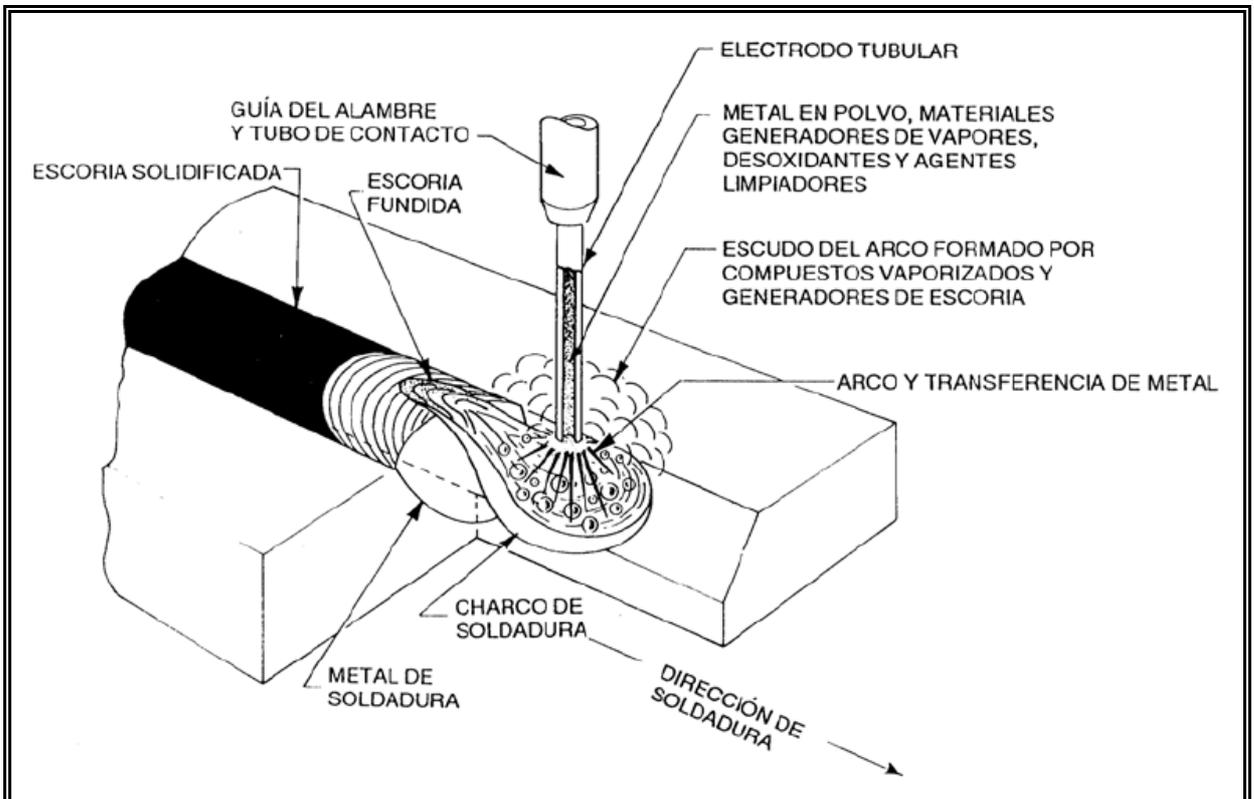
Soldadura por arco con núcleo de fundente y autoprotección.
